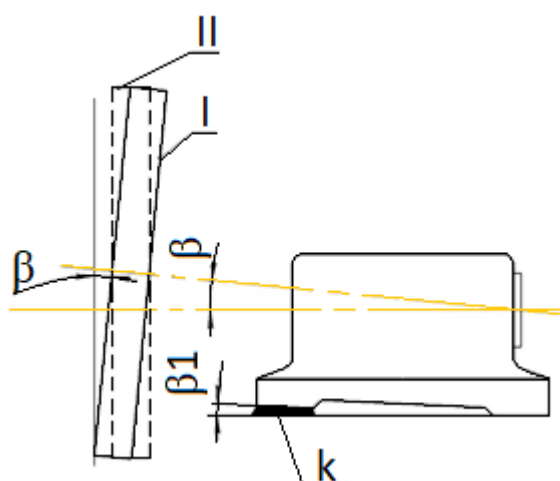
Схема регулировки положения корпус электродвигателя – станина
